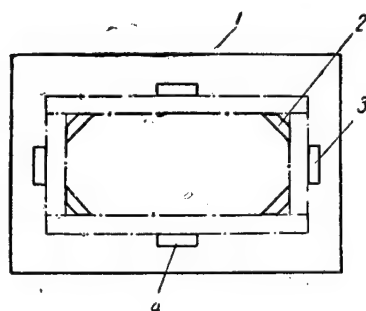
Кондуктор для сборки прямоугольных фланцев.
